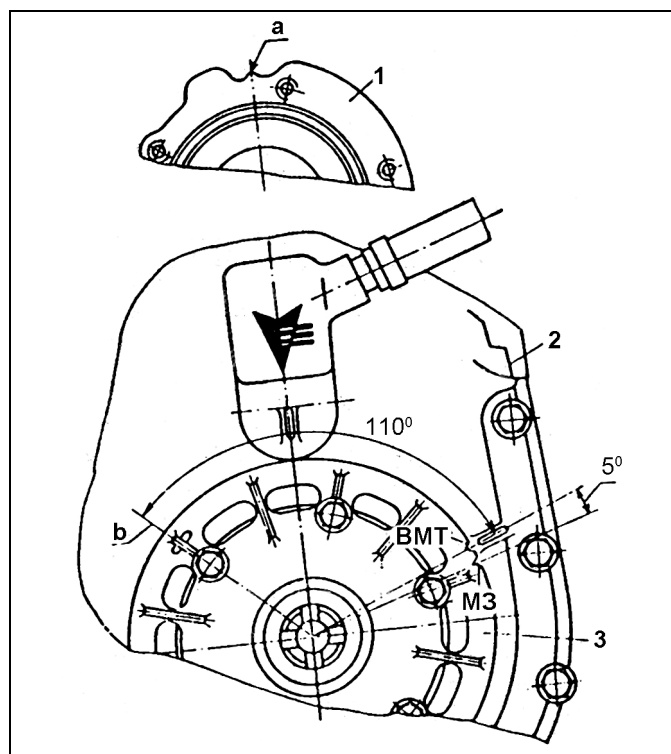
Установочные метки на крышках центробежного маслоочистителя и распределительных шестерен: а - выступ на корпусе центробежного маслоочистителя, указывающий положение ВМТ первого цилиндра; б - ось смещенного отверстия для правильной установки крышки центробежного маслоочистителя на корпус; 1 - корпус центробежного маслоочистителя; 2 - крышка распределительных шестерен; 3 - крышка центробежного маслоочистителя.
